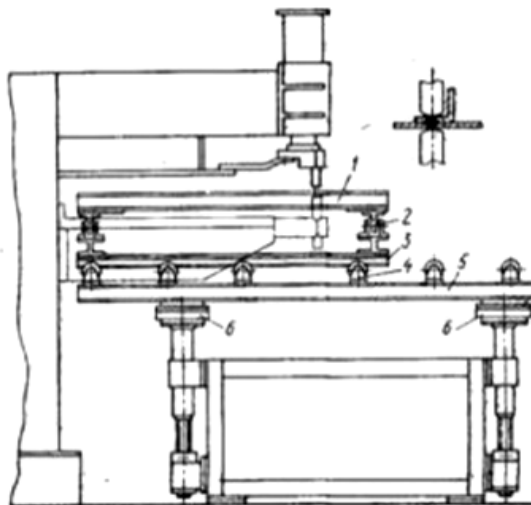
Поддерживающее устройство для точечной сварки:
